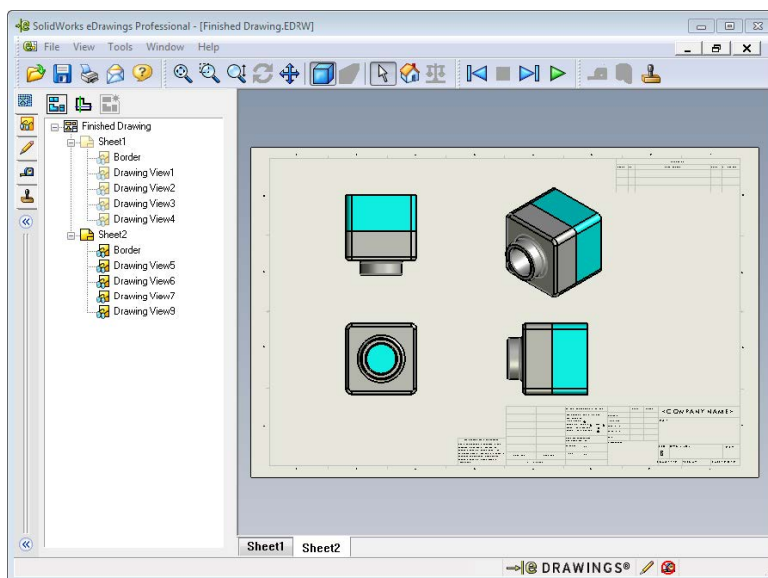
Вкладка Sheet2 (лист 2) с чертежом
